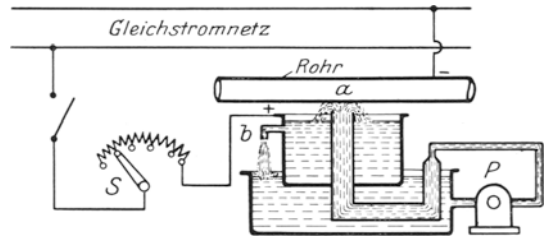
Schweißen einer Rohrlängsnaht durch Elektrolyse.
